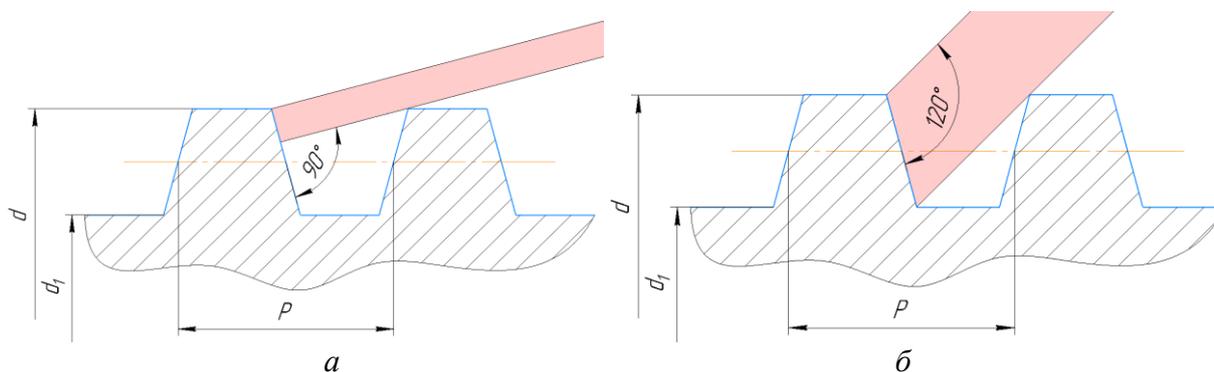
Наибольшая обрабатываемая ширина лазерным лучом:
